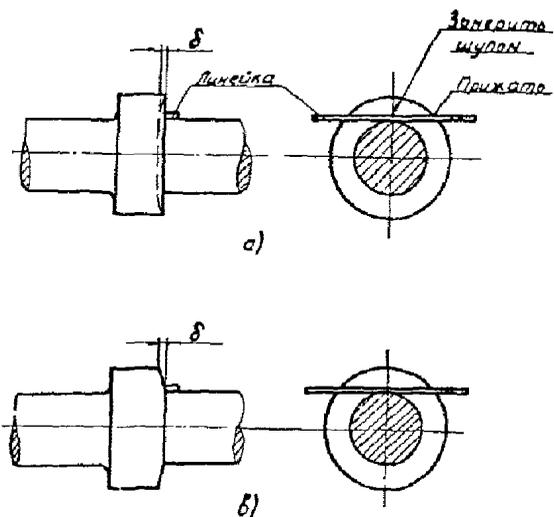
Проверка конусности рабочей поверхности упорной гребней:
